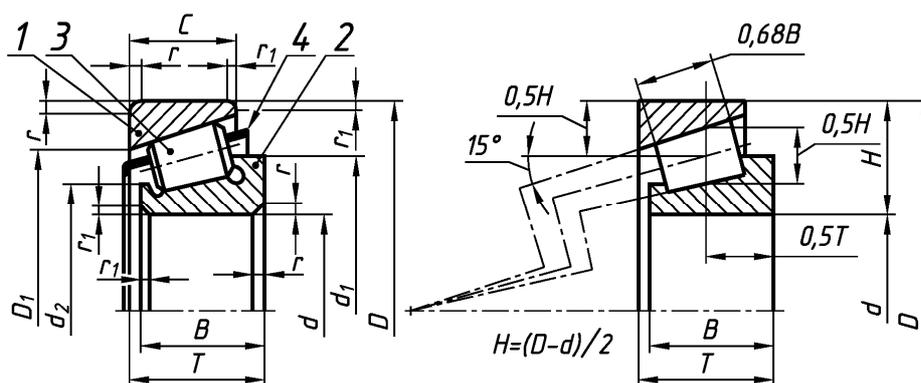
Подшипник роликовый конический радиально-упорный однорядный
